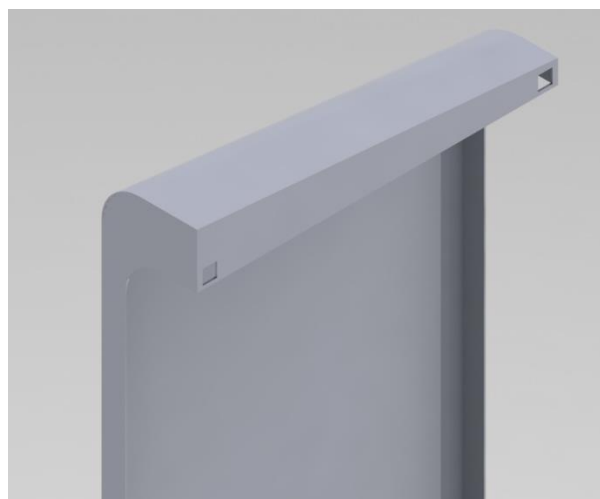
Ensamblaje subconjunto 1.1. Soldadura 5, 6 y 7.
